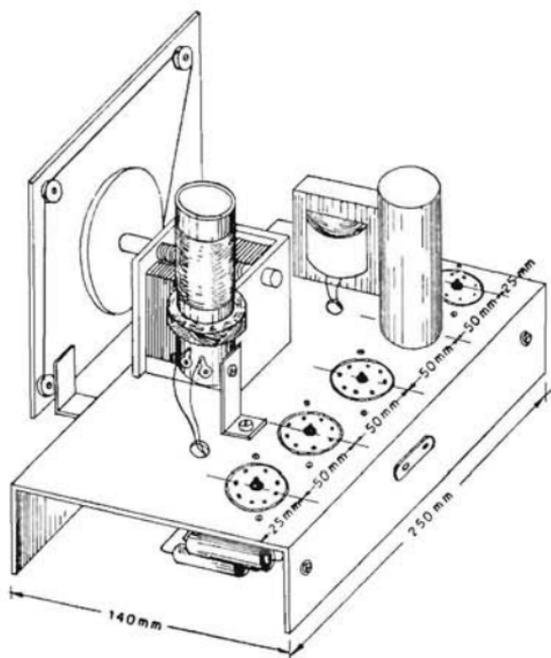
Disposizione delle parti sopra il telaio.
